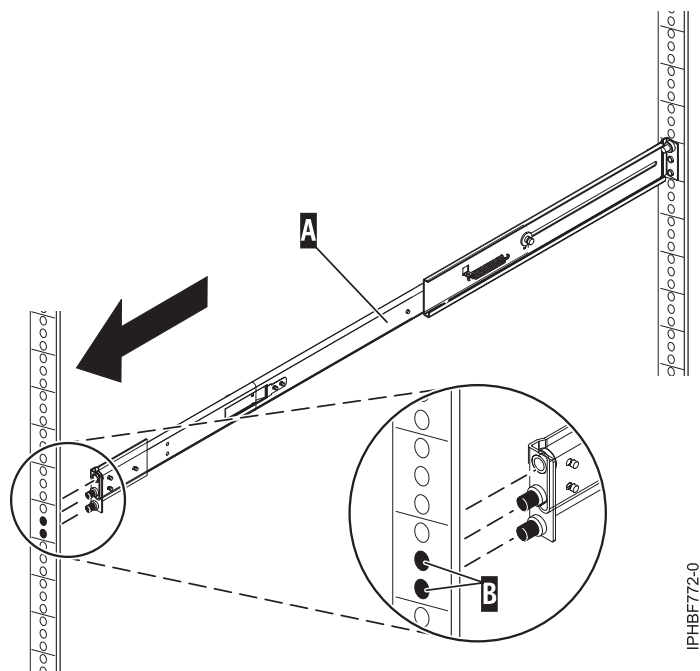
Instalando o Trilho Deslizante Direito na Parte Frontal do Rack
